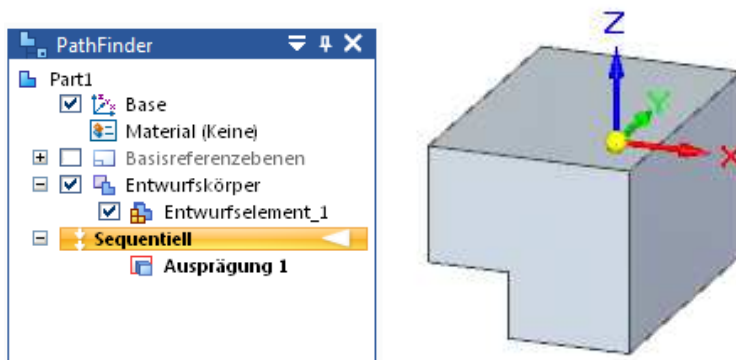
Die Ausprägung im Pathfinder und in der Ansicht
